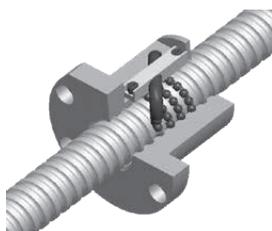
Kugelgewindemutter mit externer Kugelrückführung
